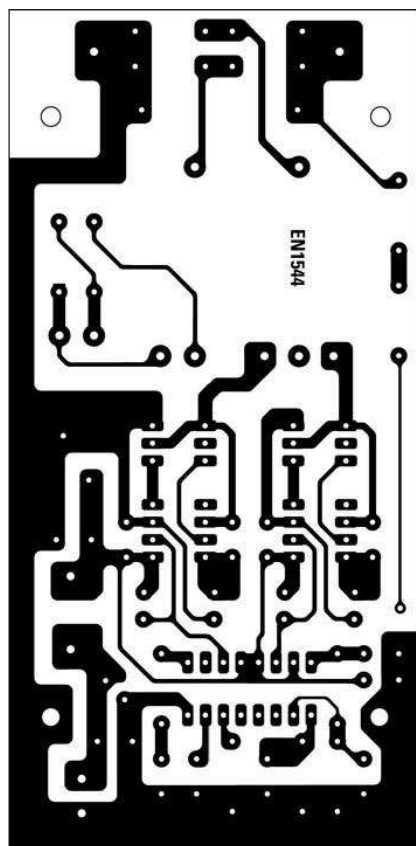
2: Dessin, à l'échelle 1, du circuit imprimé de l'étage alimentation, côté soudures.
